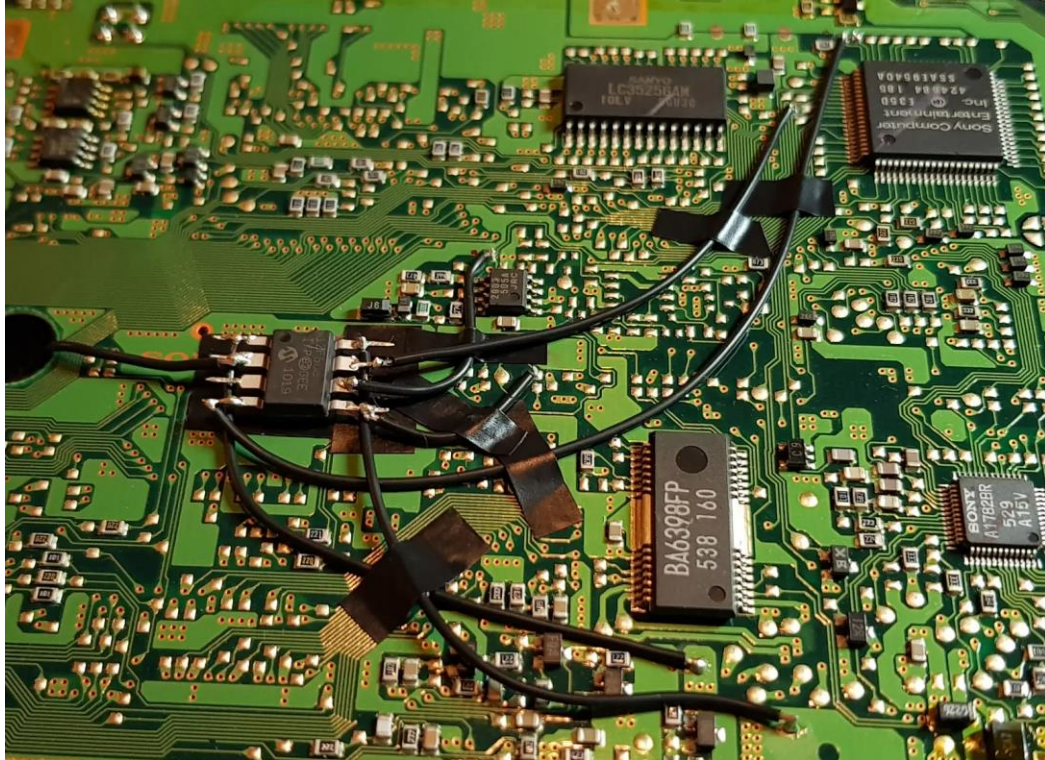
Chip Stealth 2.8a soldado a la placa madre de la PS1
